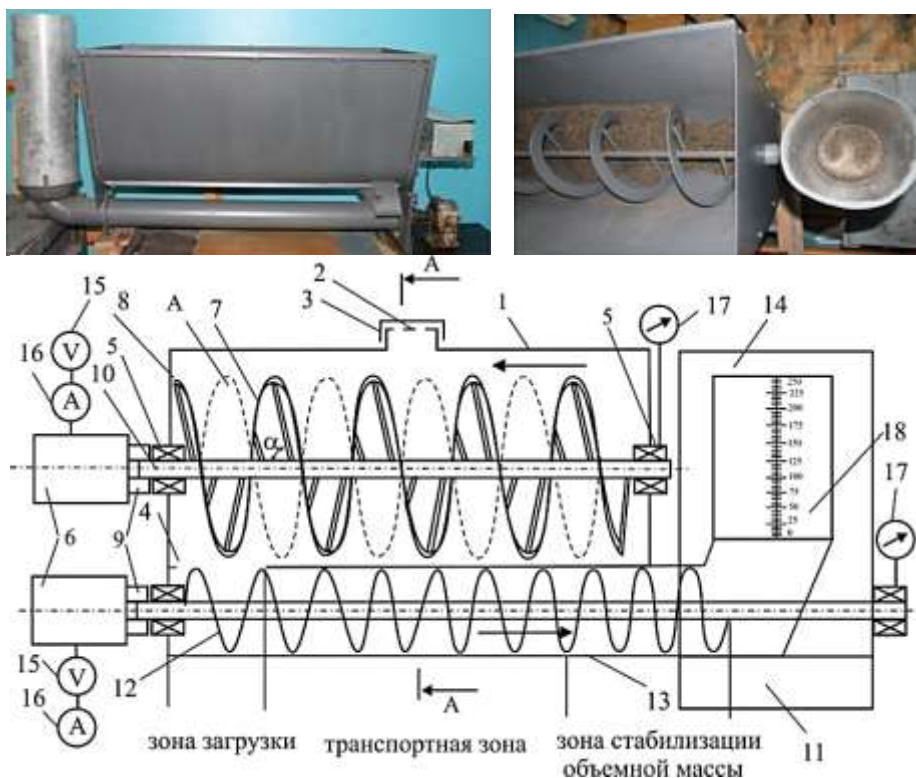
Схема и стенд (макет конструкции) питателя автомобильного газогенератора:
